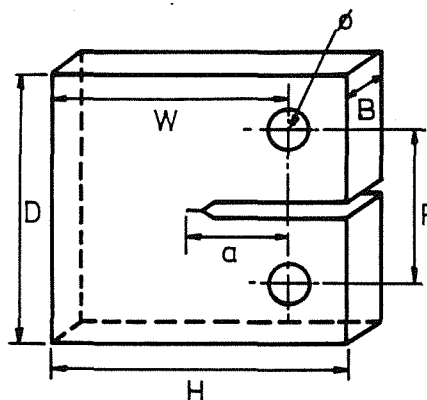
Dimensiones de las probetas C.T. B=6mm, W=23mm, a=11.35mm, P=16.66mm, H=28.75mm, D=27.6mm, Ø=5.75mm.
